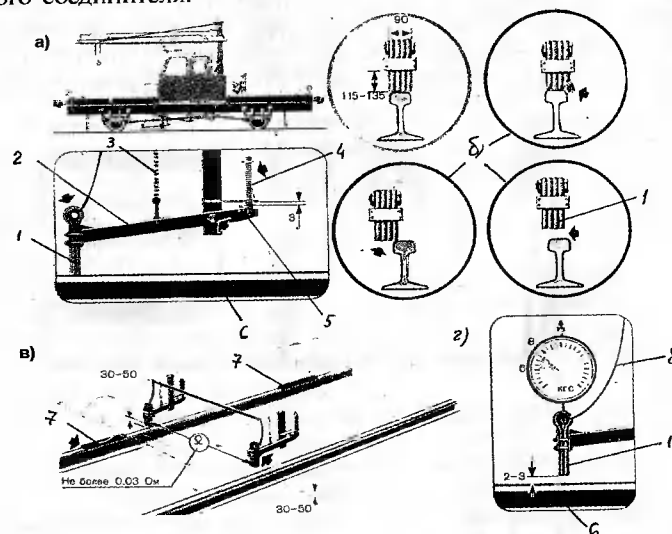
Общий вид шунтирующего устройства (а), дефекты не допускаются (б), проверка сопротивления шунтирующего устройства (в), проверка давления щетки на рельс (г): 1 — щетки; 2 — поворотный рычаг шунтирующего устройства; 3 — цепь предохранительная; 4 — пружина; 5 — винт упорный; 6 — рельс; 7 — изолирующие прокладки; 8 — электрический соединитель
